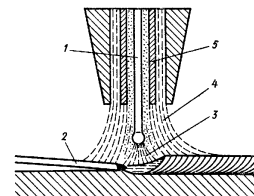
Схема дуговой сварки с комбинированной защитой:
